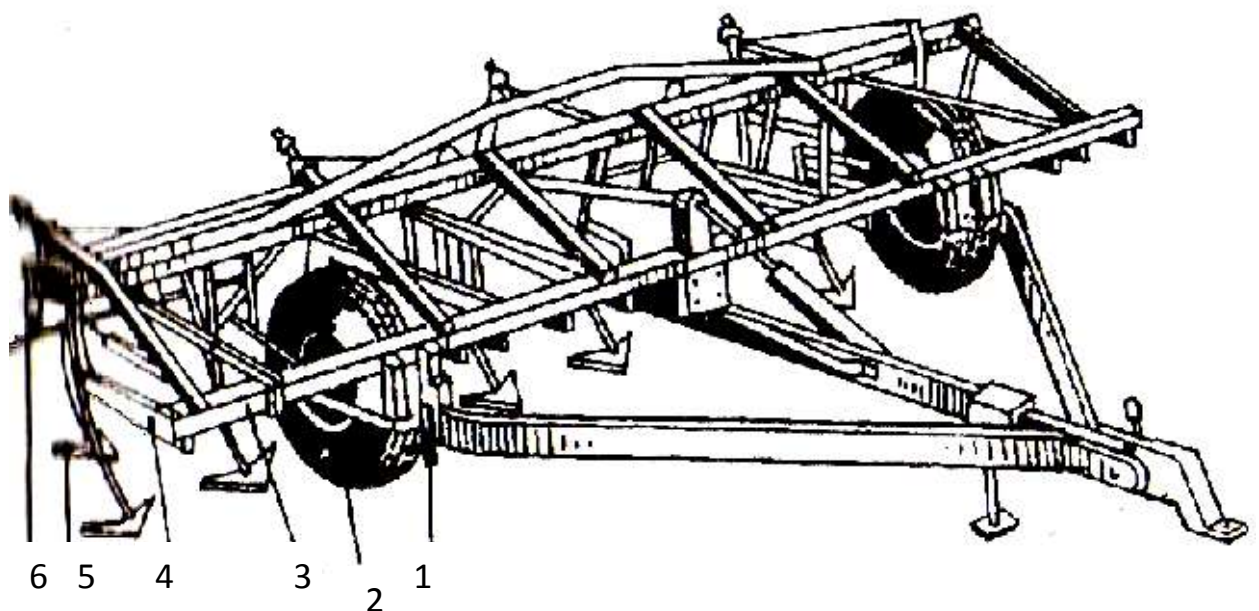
Культиватор КПС-4А: 1 – регулятор глубины; 2 – опорное колесо; 3 – рама; 4 – грядили; 5 – лапа; 6 –
